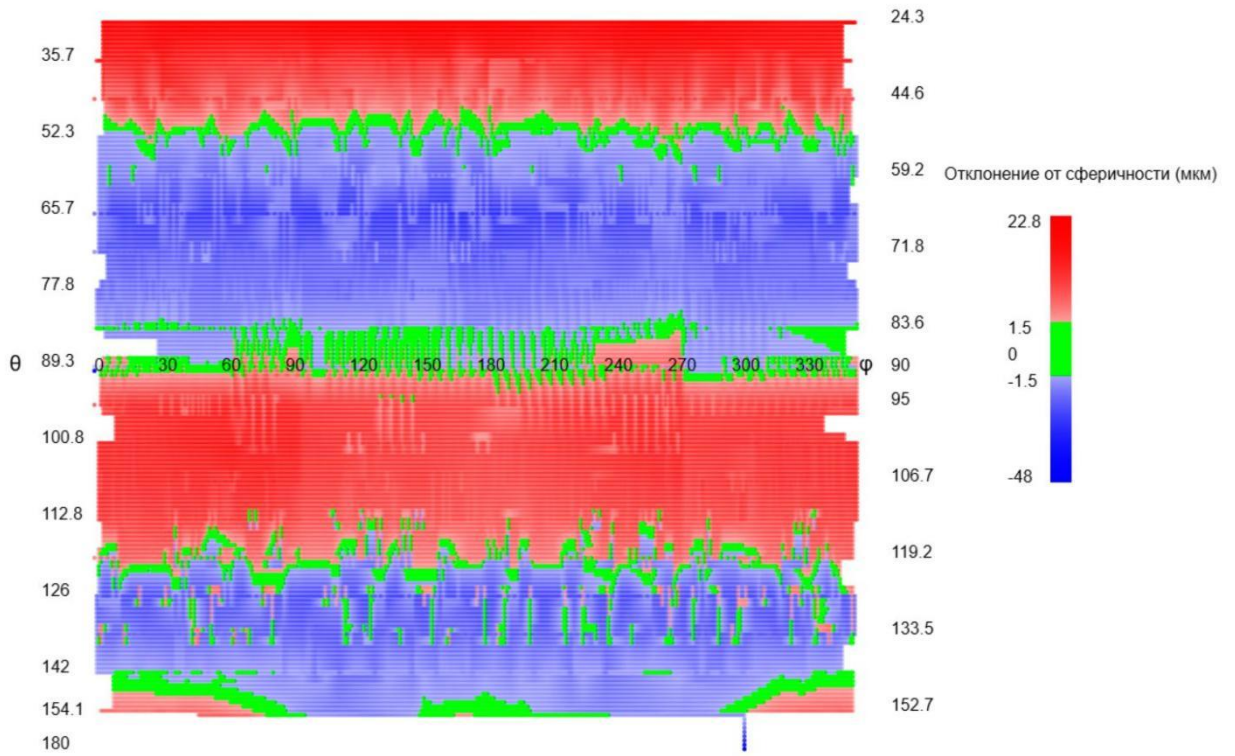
Развертка сферической поверхности шарового пальца №1 до притирки
